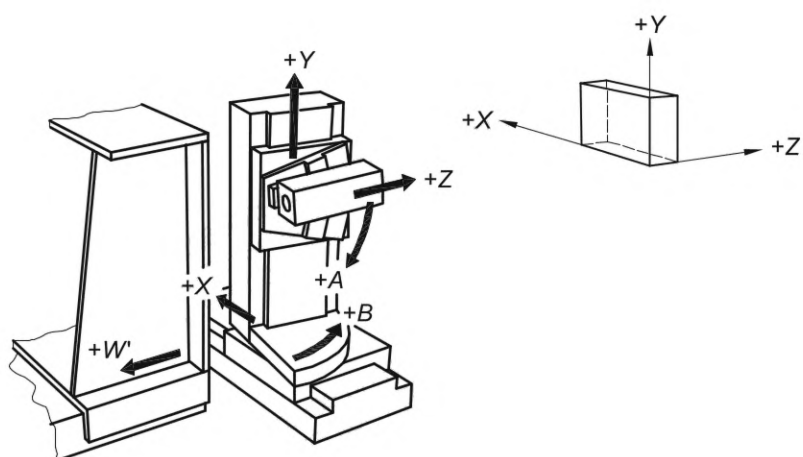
Контурно-фрезерный станок с горизонтальным шпинделем
